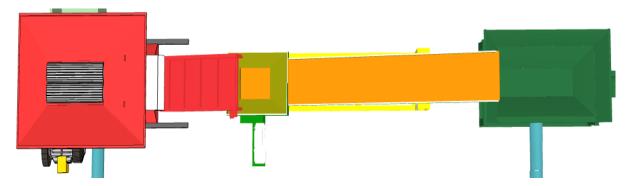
Vu en 3D du broyeur et du silo de pré-stockage.
